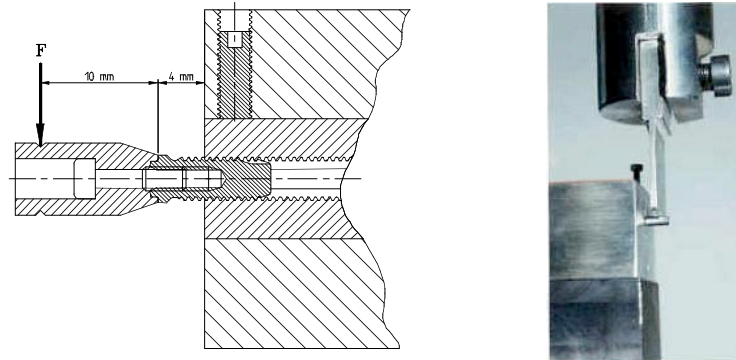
Caricamento dell'impianto a 90°
